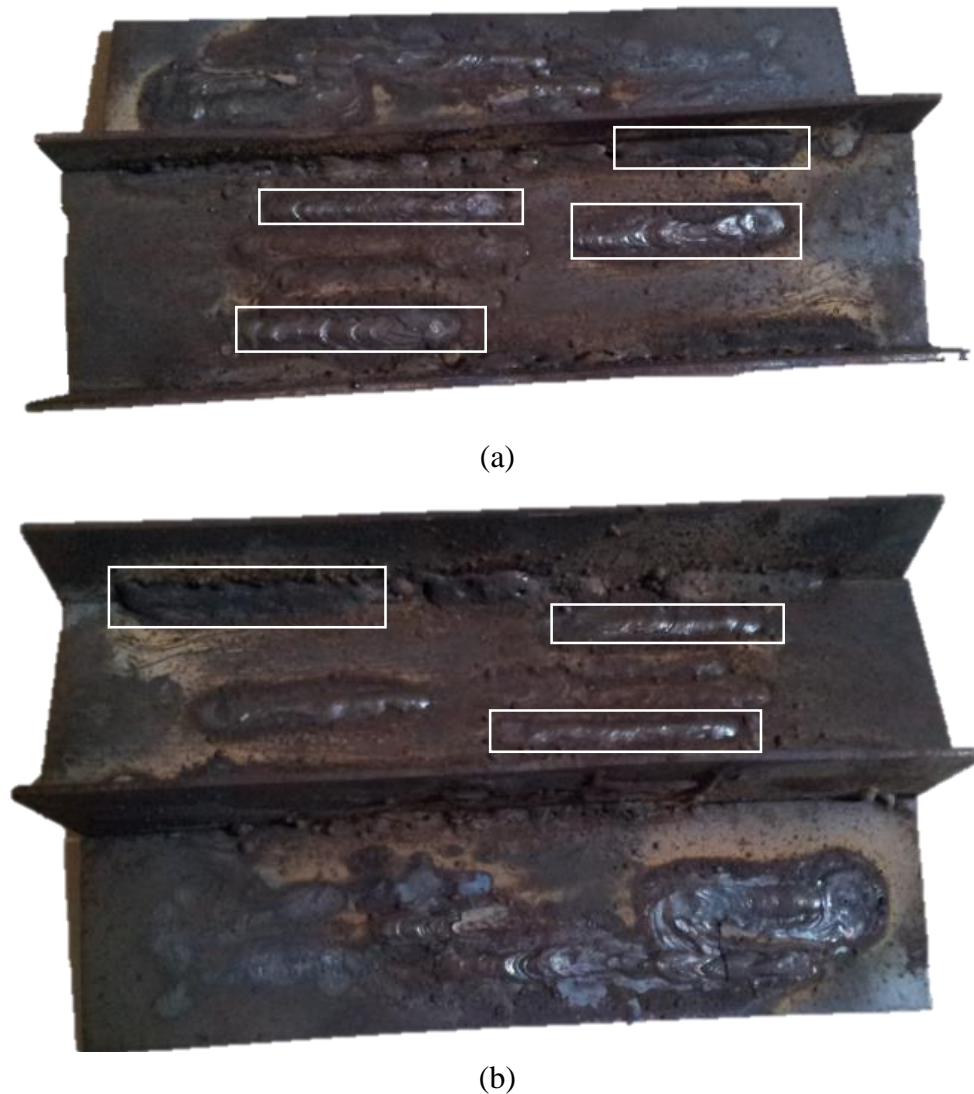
Peça utilizado durante o processo de soldagem.
